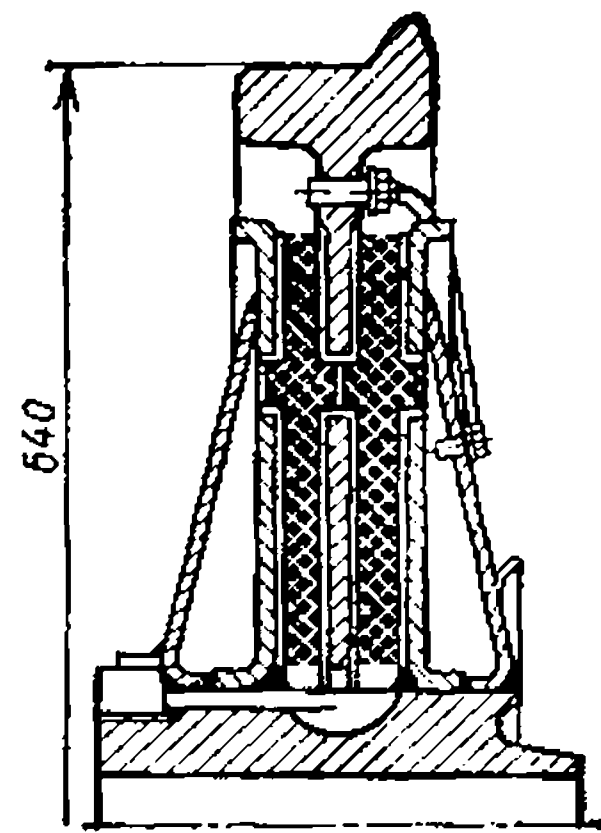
Колесо трамвая Tatra с цилиндрическим профилем поверхности катания и резиновыми вкладышами
